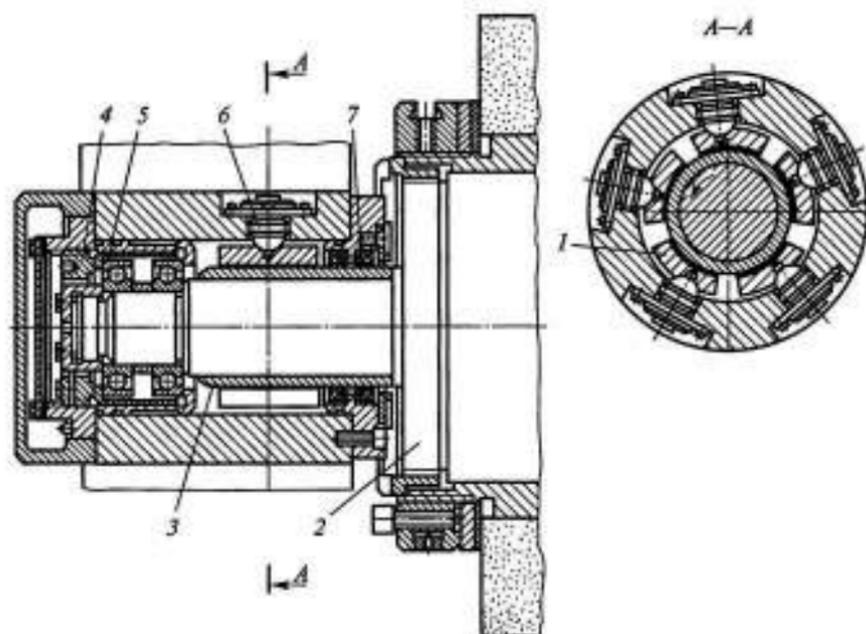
Опора шпинделя шлифовального круга с гидродинамическим пятикладышным подшипником:
